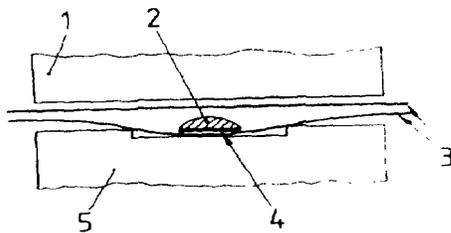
Магнитный блок с металлической крышкой (размеры в мм)
